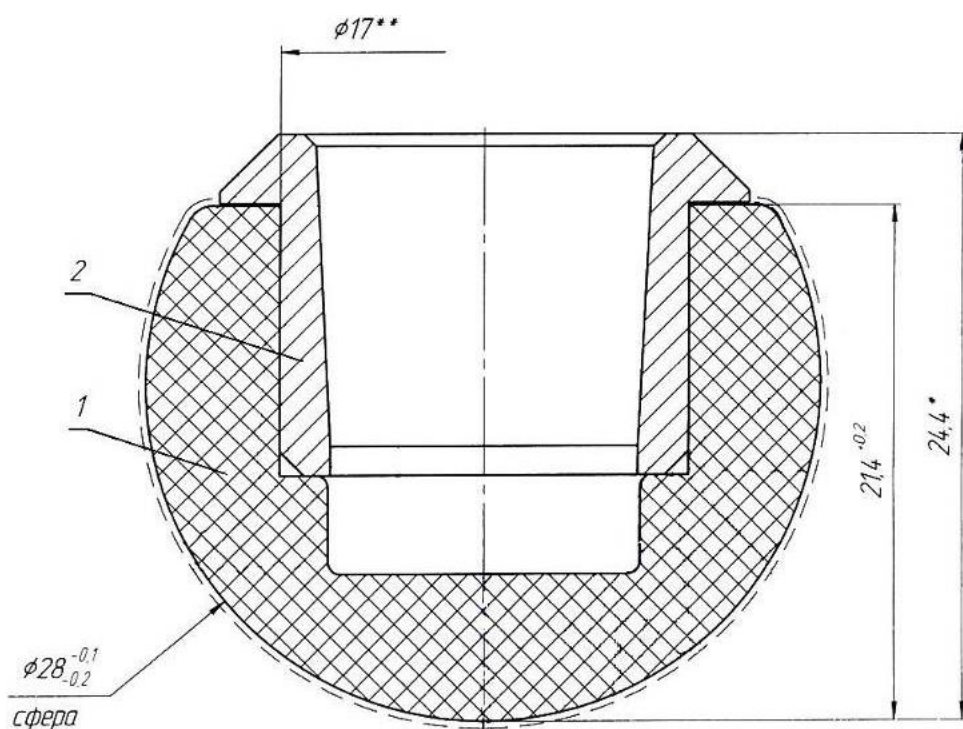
Эскиз головки эндопротеза из углеситалла диаметром 28 мм:
